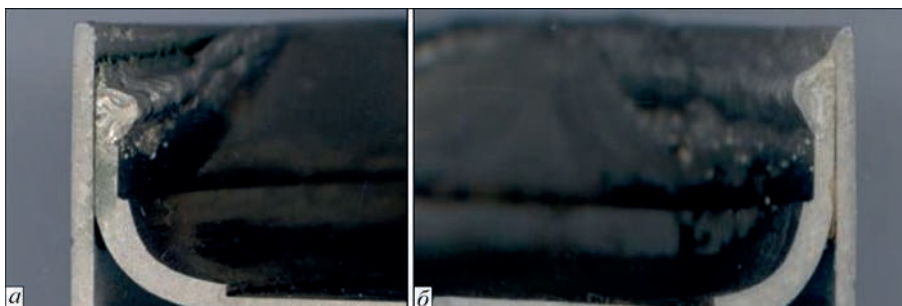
Дефекти формування зварного з'єднання, спричинені порушенням технологічного режиму складання та зварювання: *a* – стікання металу шва по внутрішній бічній стінці; *b* – втрата форми шва, підріз внутрішньої кромки
